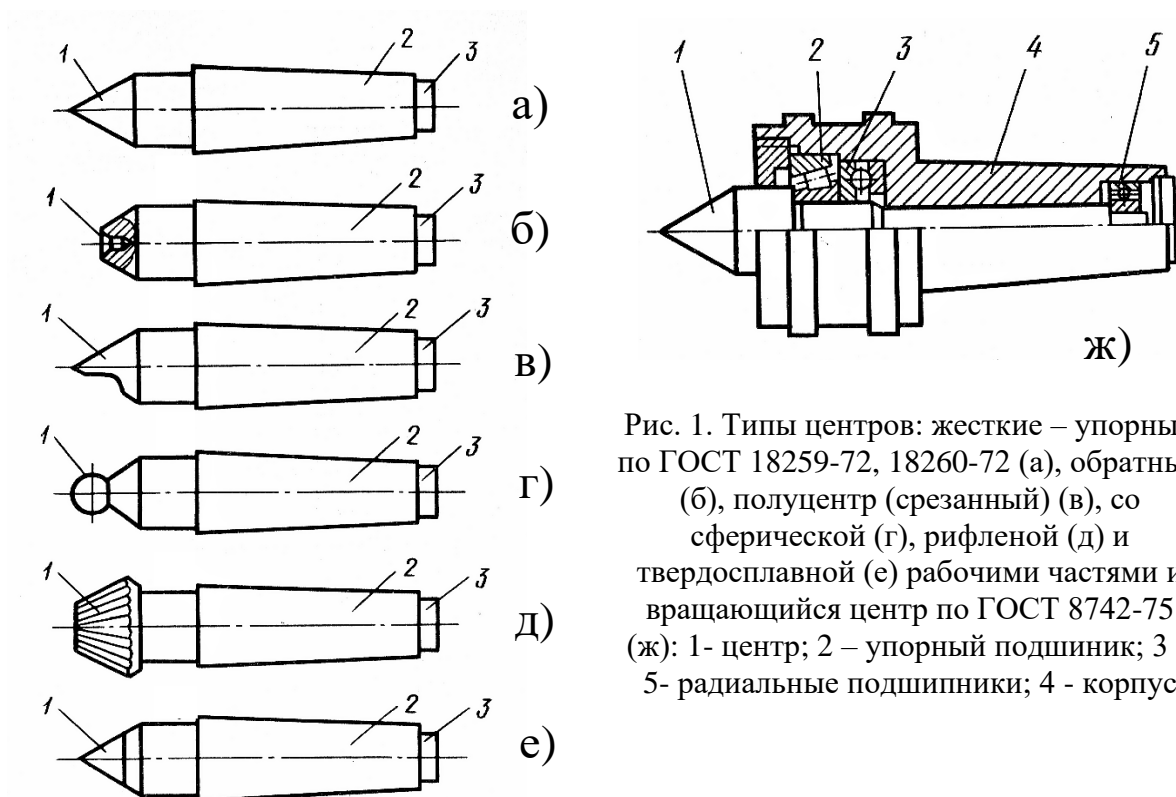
Типы центров: жесткие – упорный по ГОСТ 18259-72, 18260-72 (а), обратный (б), полуцентр (срезанный) (в), со сферической (г), рифленой (д) и твердосплавной (е) рабочими частями и вращающийся центр по ГОСТ 8742-75 (ж): 1- центр; 2 – упорный подшипник; 3 и 5- радиальные подшипники; 4 - корпус
